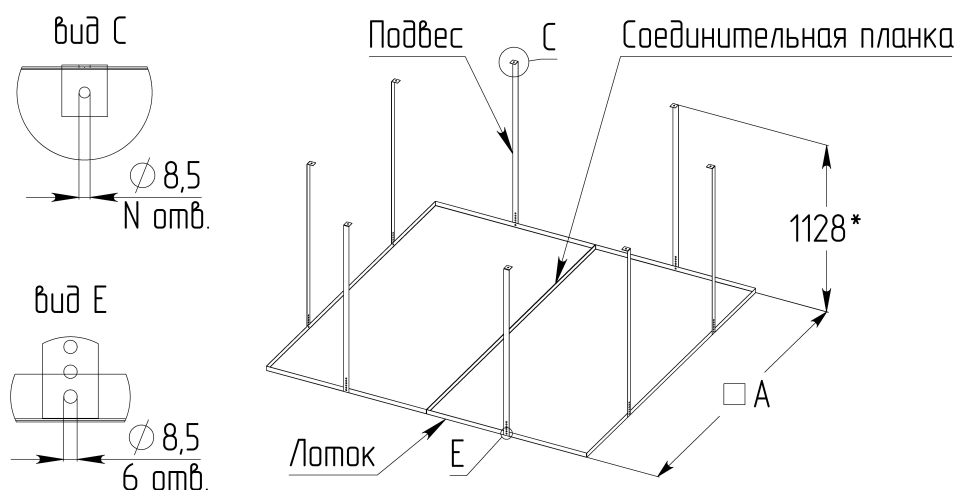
Внешний вид и размеры поддона для сбора конденсата PV
